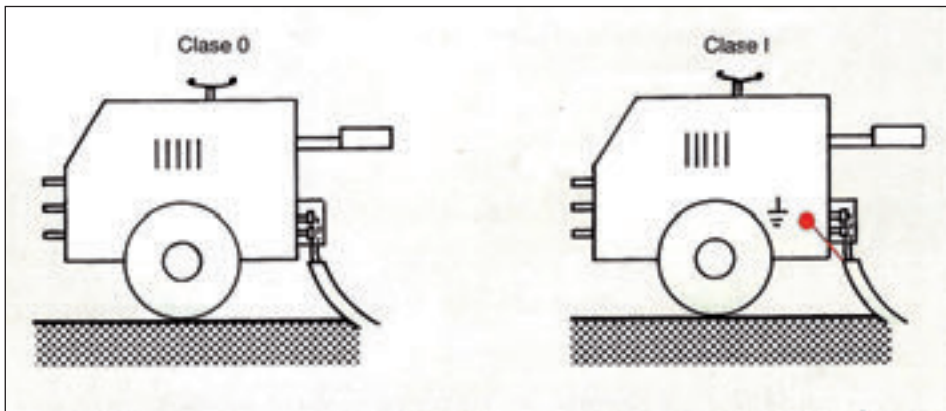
Aparatos de soldadura eléctrica, portátiles.
